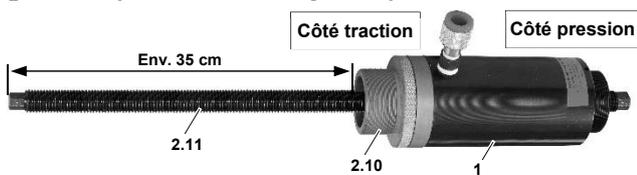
Visser le vérin hydraulique dans la plaque de base. Dévisser l'écrou de serrage.
